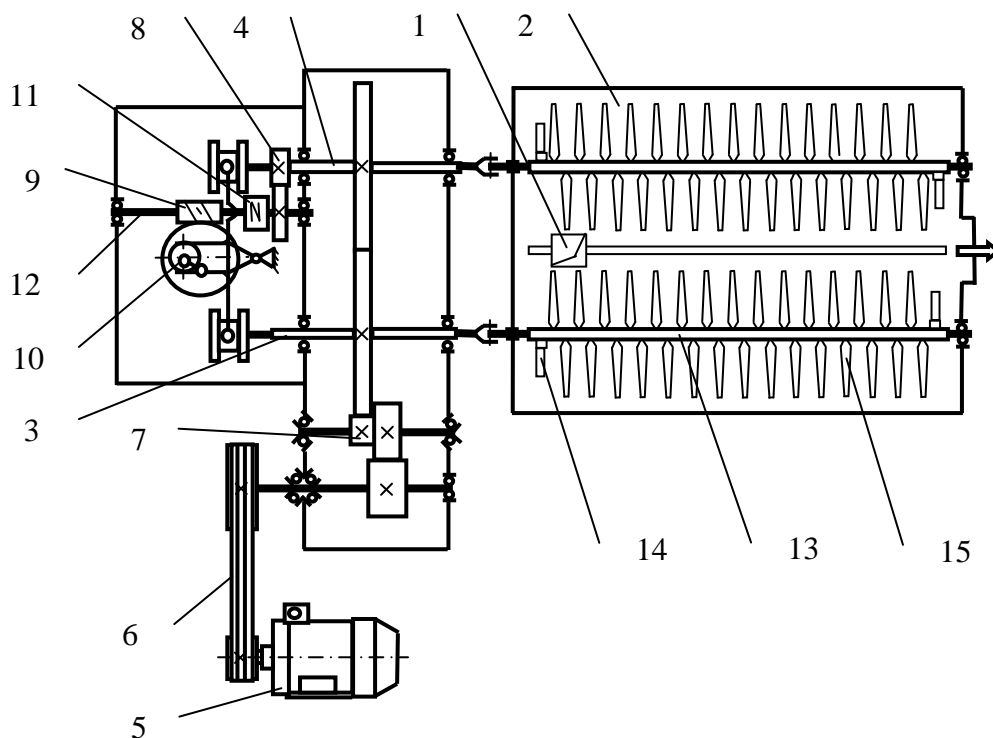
Кинематическая схема двухвального смесителя: 1 – загрузочный патрубок; 2 – рабочая камера; 3, 4 – приводные валы; 5 – электродвигатель; 6 – ременная передача; 7 – двухступенчатая зубчатая передача; 8 – одноступенчатая зубчатая передача; 9 – червячная передача; 10 – механизм возвратно-поступательного движения; 11 – предохранительная муфта; 12 – вал, 13 – рабочий вал (2 шт.), 14 – скребковые лопатки (4 шт.), 15 – месильные лопатки (60 шт.)
